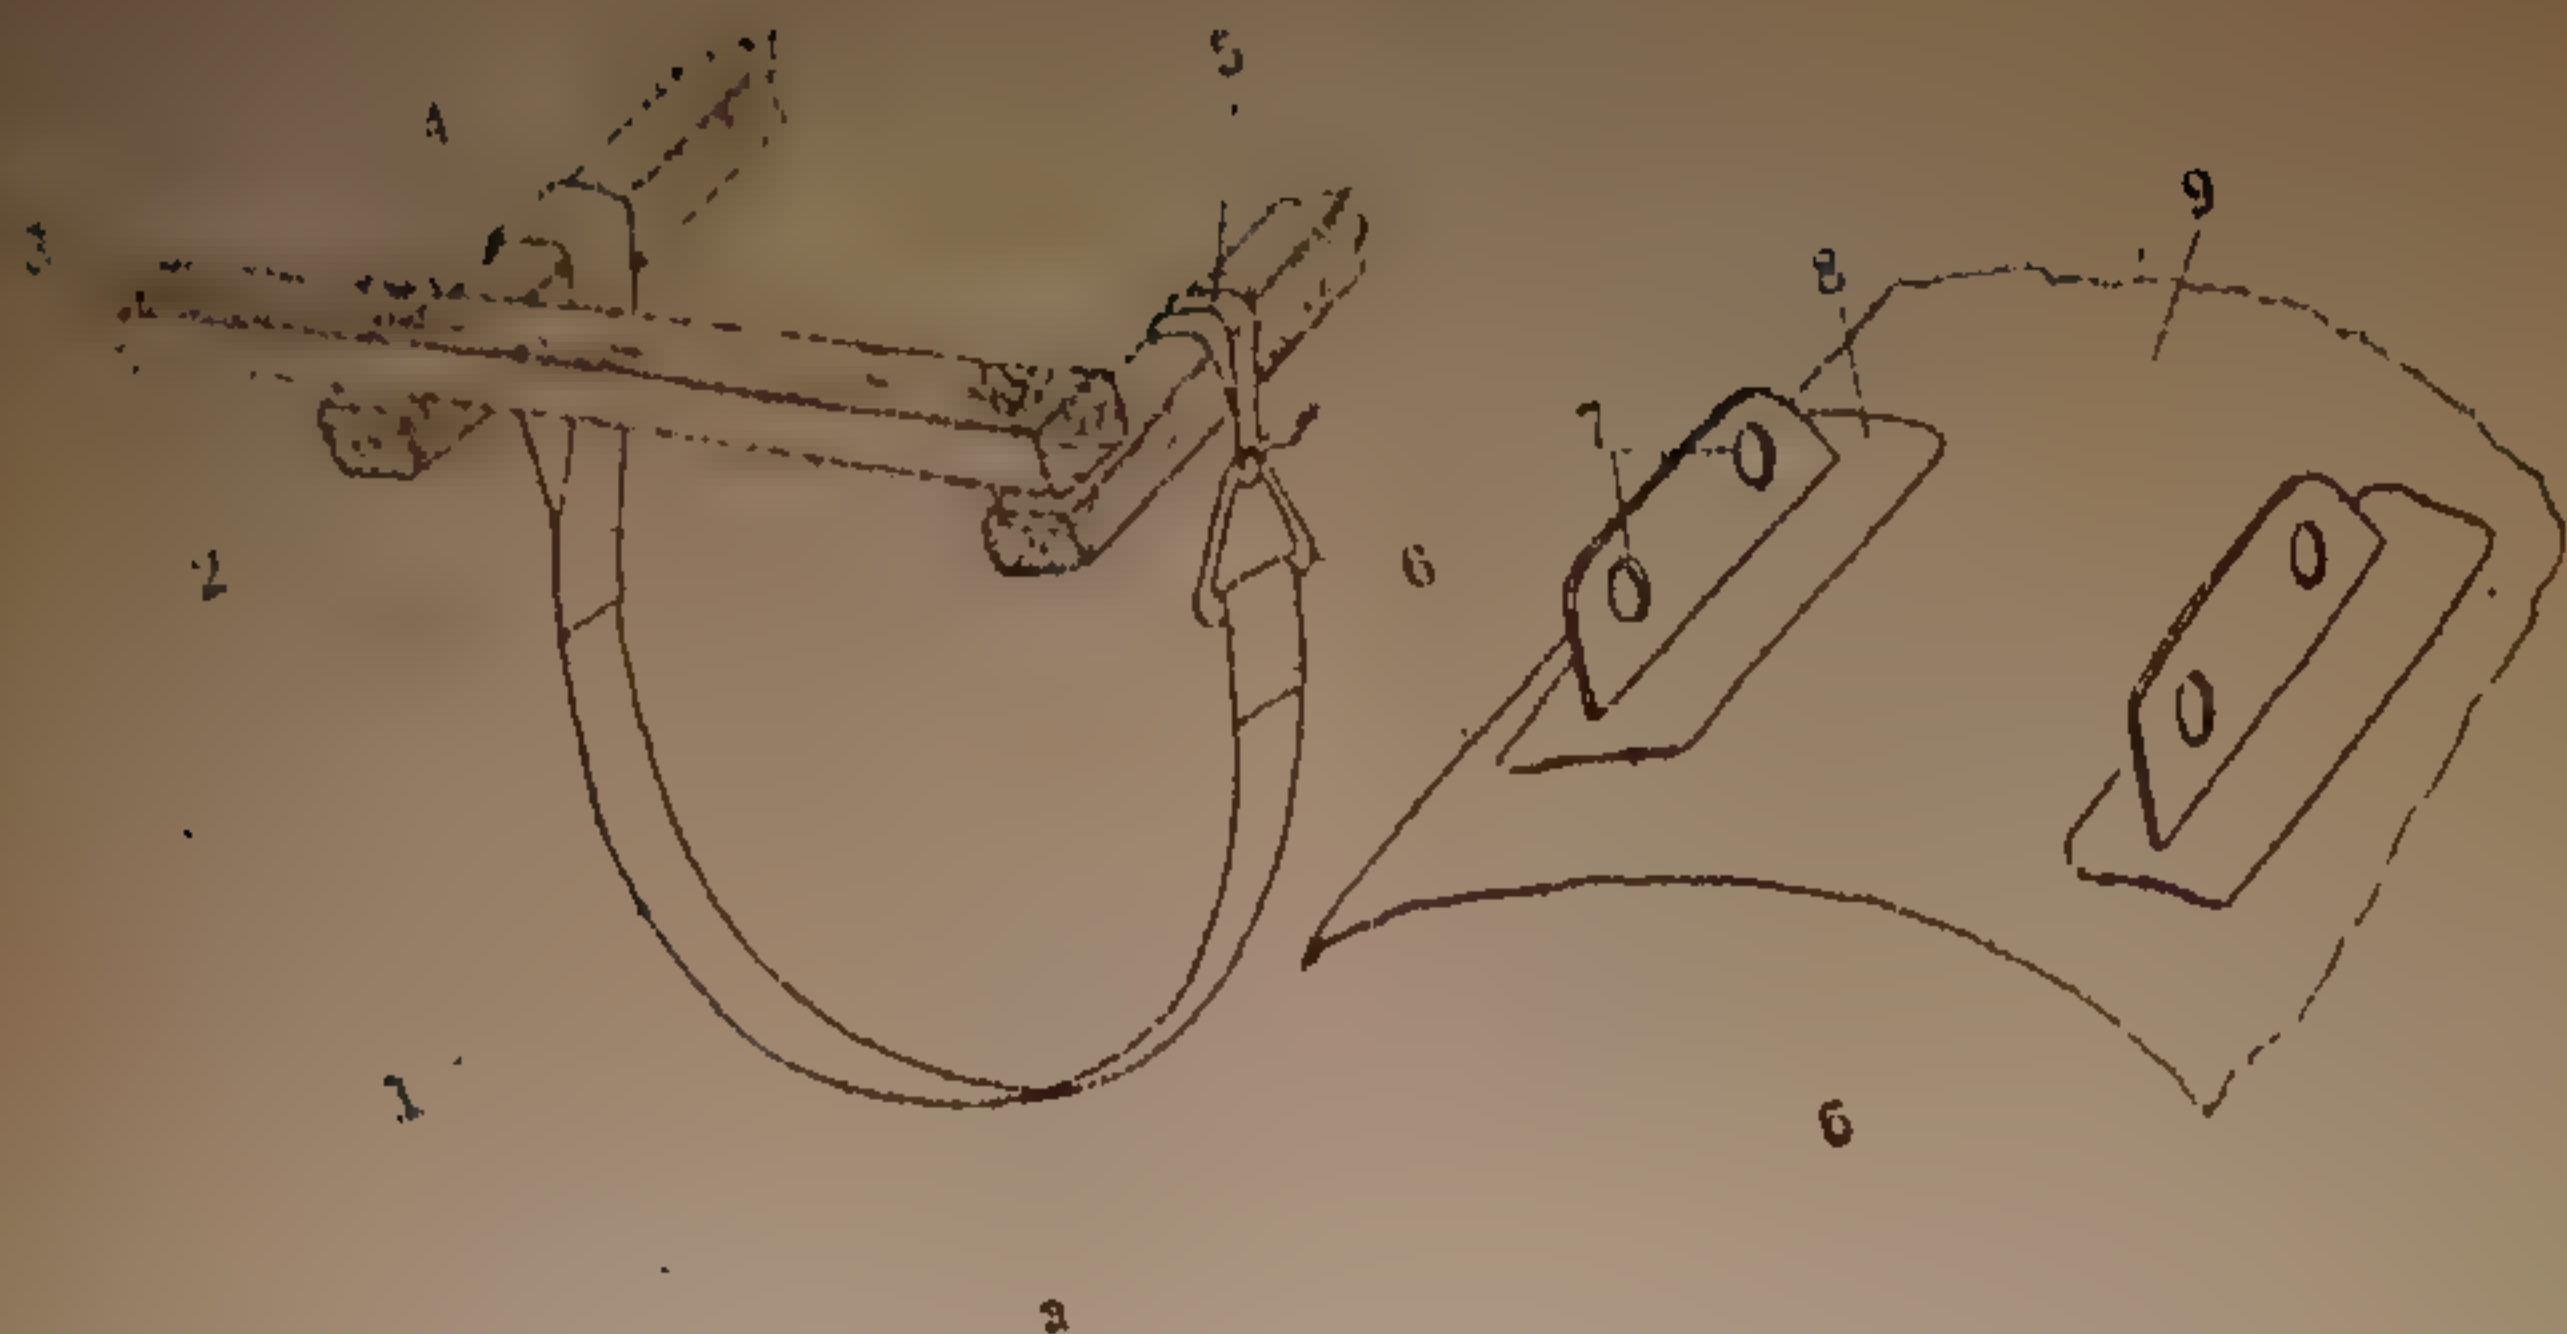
Способы крепления баллонов к платформе: а — с помощью ленты; б — с помощью накладок с люверсами; 1 — лента; 2 — продольный брус платформы; 3 — поперечная балка; 4 — болт с шайбами и барашком; 5 — шнур; 6 — скоба из стальной проволоки; 7 — люверсы; 8 — накладка из прорезиненной ткани; 9 — поверхность баллона
